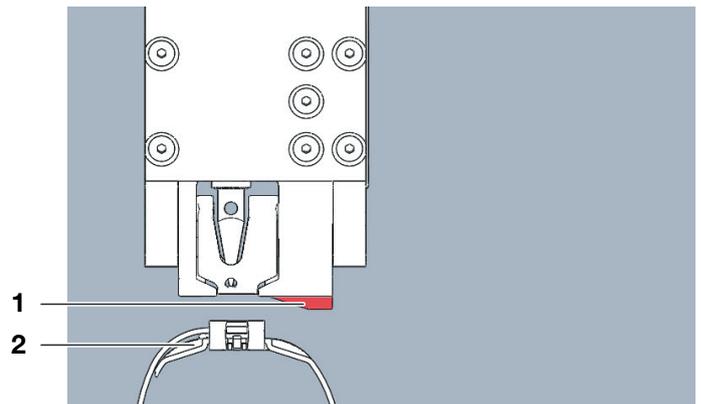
Ausrichtung des Positionierkeils des Prüfkopfs mit Messschnabel
